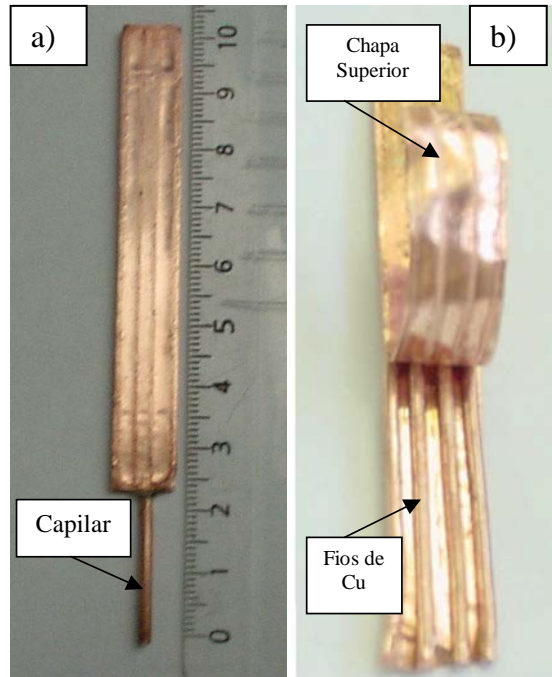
Micro tubo de calor de fios. a) Micro tubo após soldagem. b) Detalhe interno do micro tubo.
